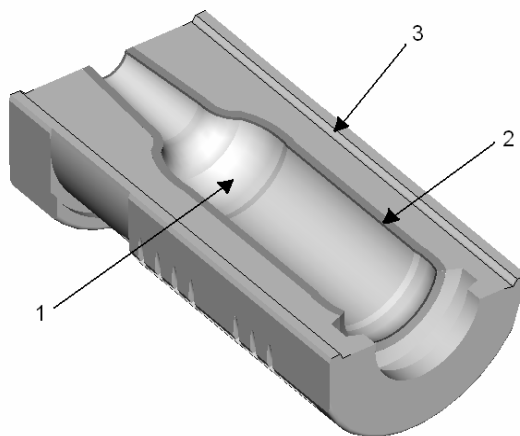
Чистовая полуформа (0,5 л): 1 – формирующая поверхность;
